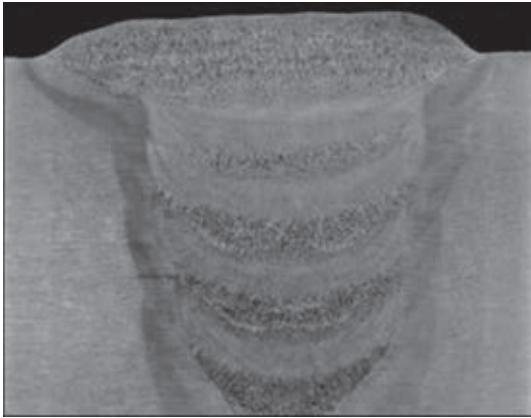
Макрошлиф (увелич. 3,5) сварного соединения, выполненного рутиловой порошковой проволокой
